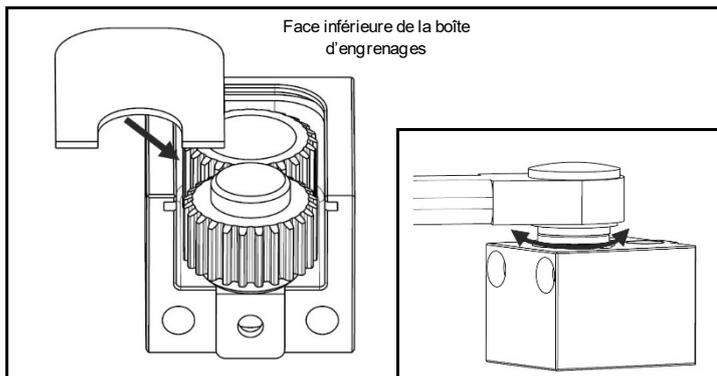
Installer le couvercle de la boîte d'engrenages; vérifier que les pignons tournent correctement
